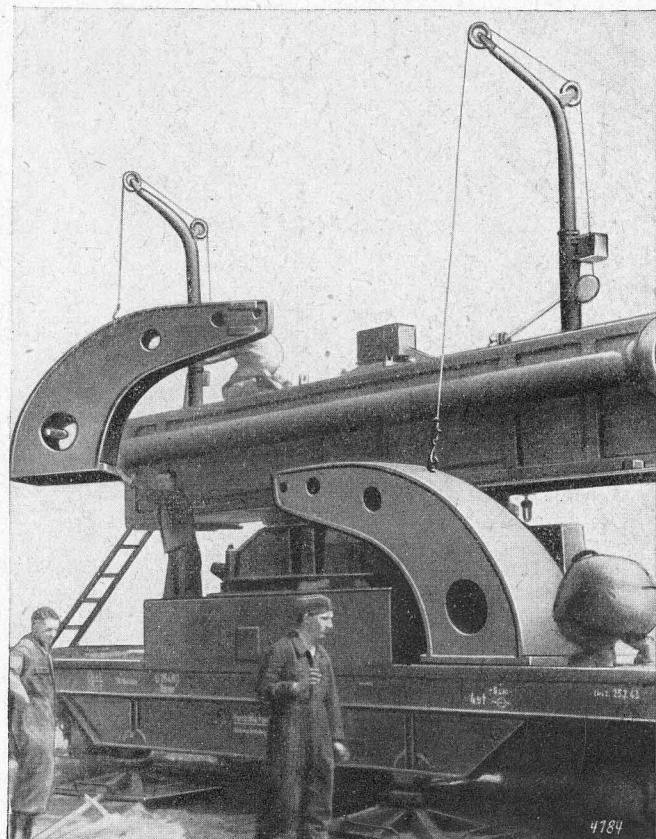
Tragarme (III/5) an den Drahtseilen der Schwenkkrane befestigen. Halteschrauben der Tragarme an der Bodenfläche des Sockelwagens lösen. Drahtseile aufwinden und durch Schwenken der Ausleger die Tragarme über die Auflageflächen am Hauptträger bewegen. Auflageflächen an den Tragarmen und am Hauptträger reinigen.
